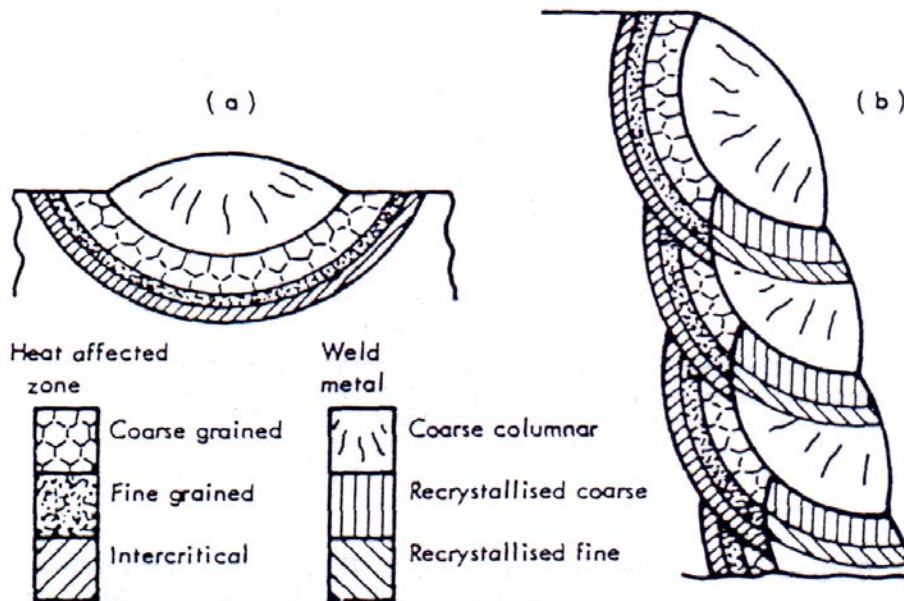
Esquema ilustrativo del efecto de un segundo cordón sobre el metal de soldadura y la zona recristalizada previa. a- monopasada. b- multipasada (33).
